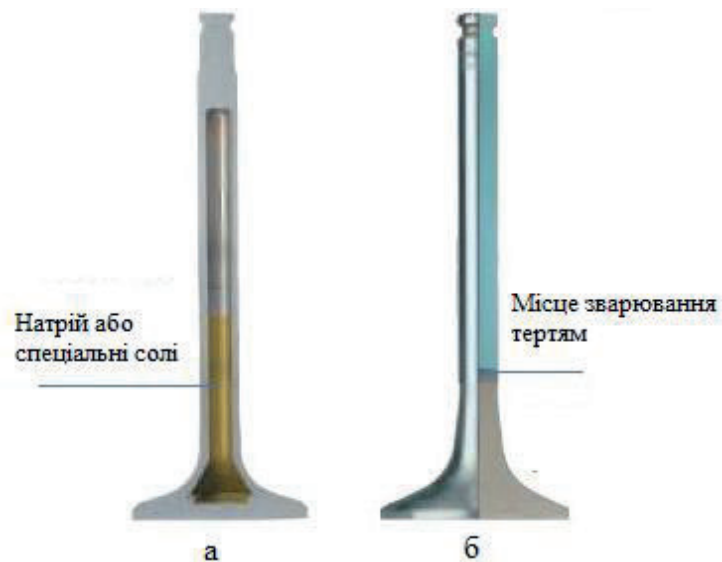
Випускні клапани з наповнювачем (а) і біметалевий (б)
